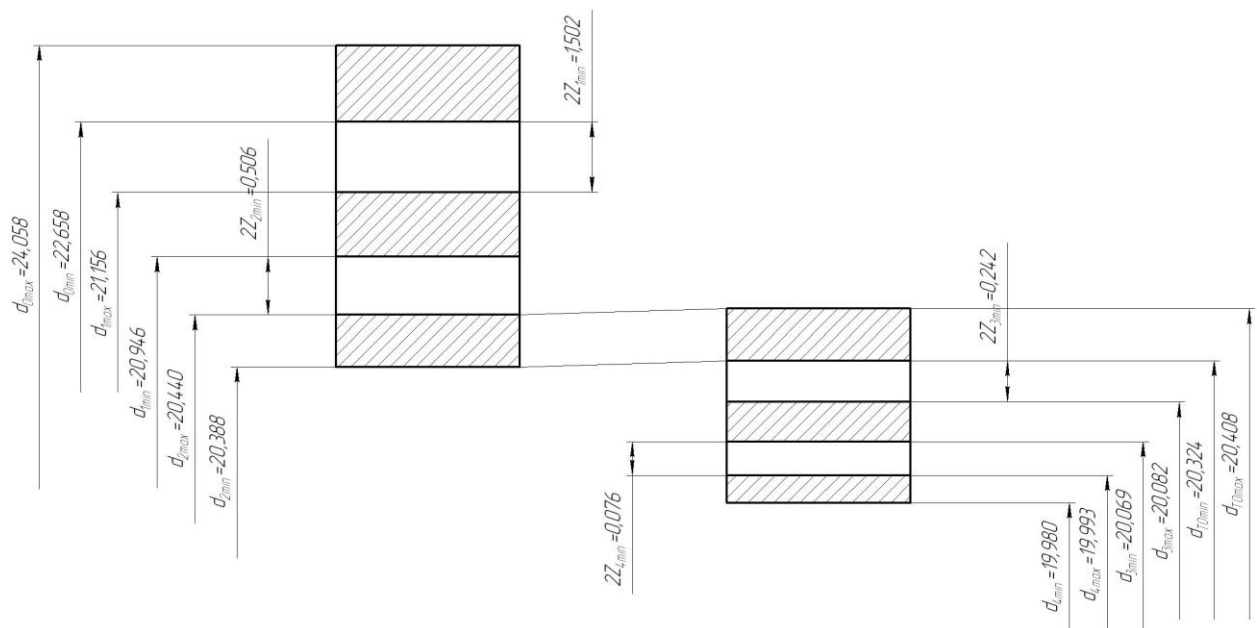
Схема расположения припусков и полей допусков
